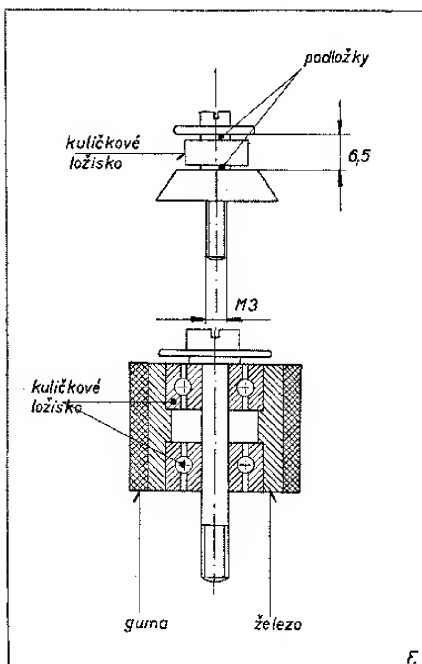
Převod pro převíjecí a navíjecí kotouče a regulátor otáček. Relé pro přetlačnou kladku.
